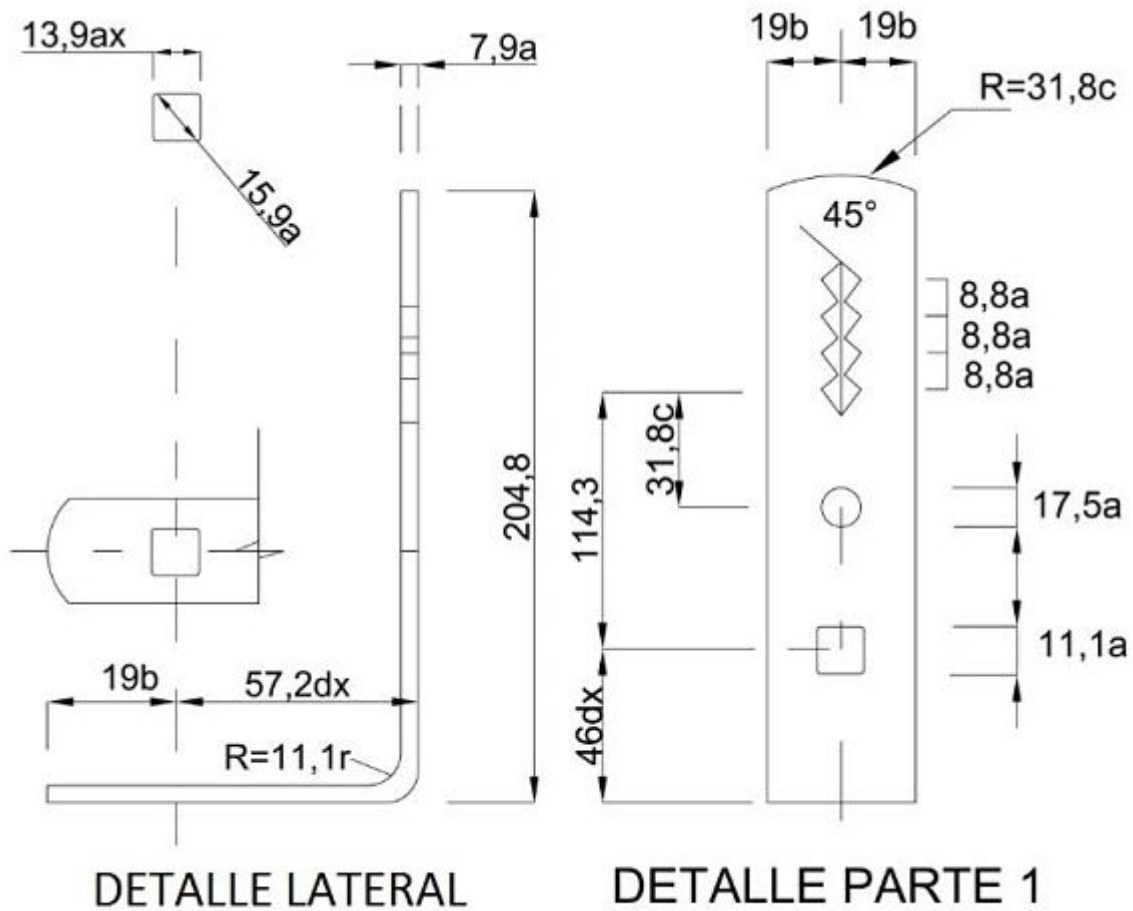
A: Soporte para fijación a cruceta, detalle parte 1. Dimensiones en milímetros [mm]
